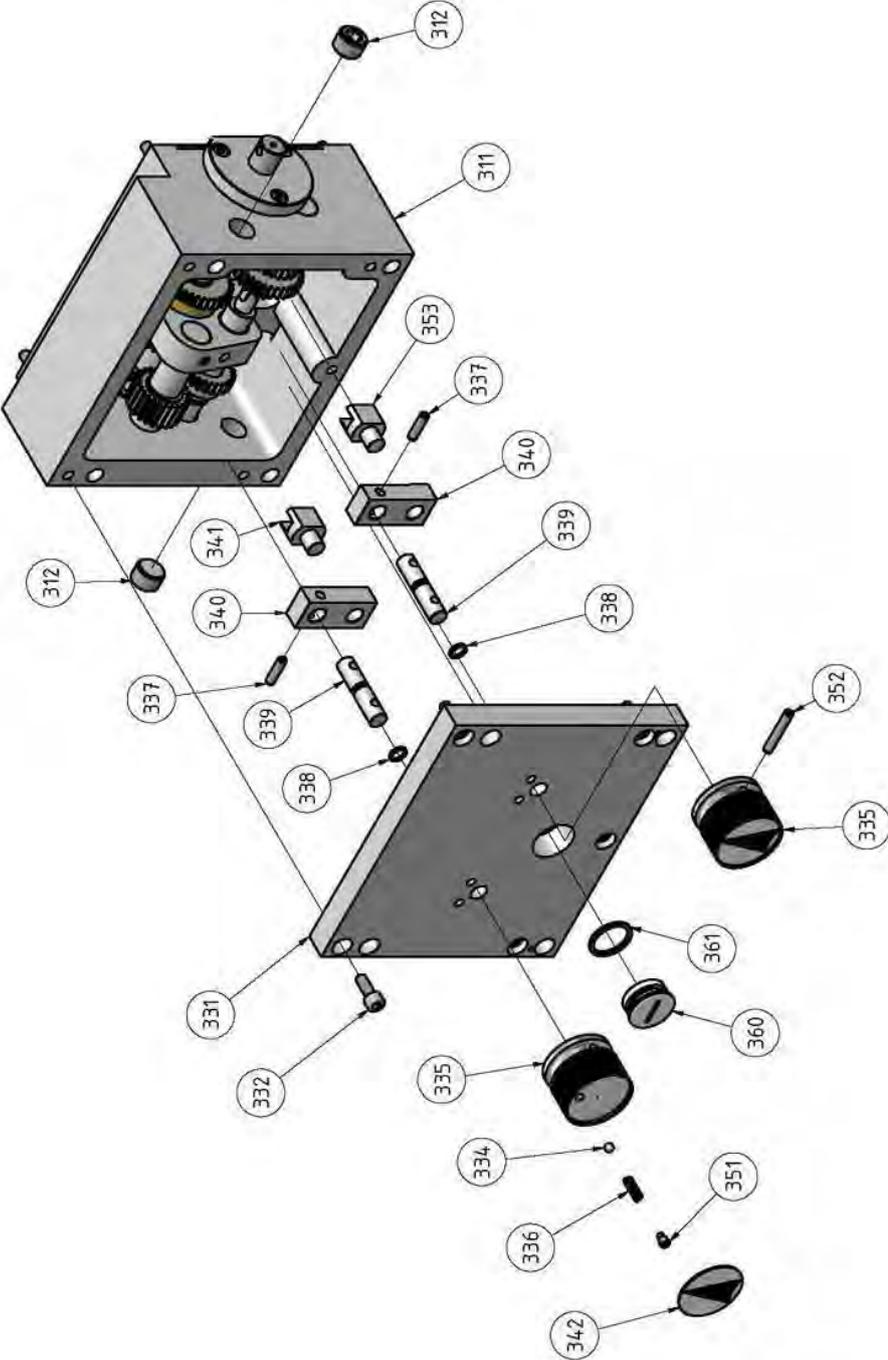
Vorschubgetriebe 1 von 2 - Engranajes de avance 1 de 2 - TU2807
